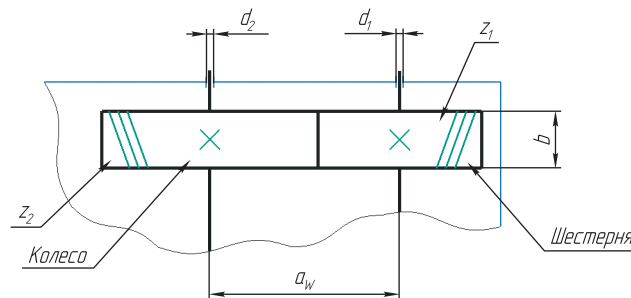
Схема цилиндрической прямозубой передачи редуктора
